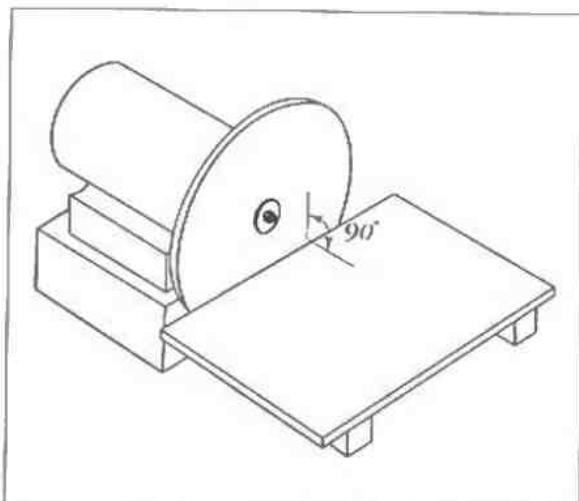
Шлифовальный круг со столиком для обработки торцов и кромок деталей
